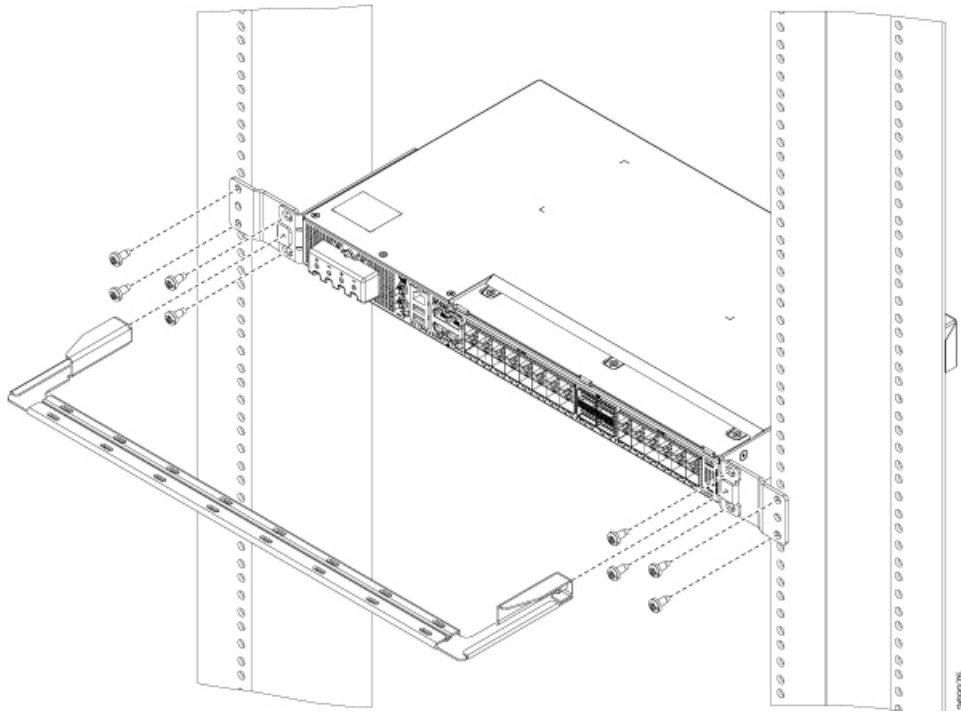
Installation des supports de montage en rack de 23 pouces au milieu
